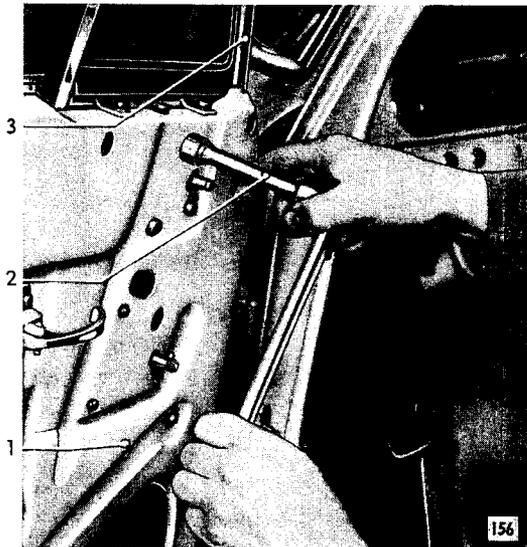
Klemmschraube für Mitnehmer am Drehfenster-Apparat herausschrauben
